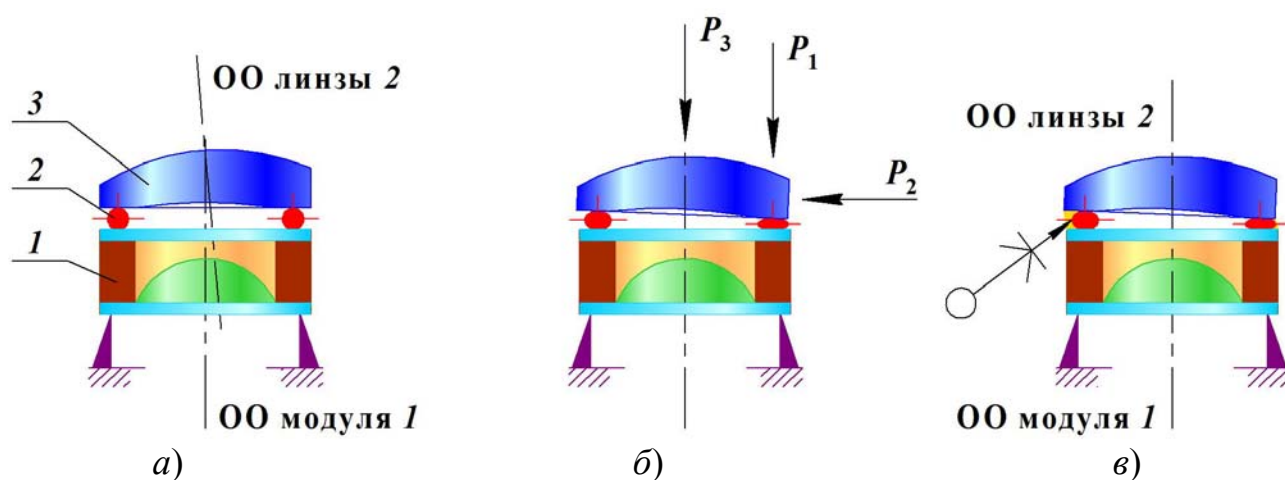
Принцип сборки и юстировки двухкомпонентного оптического блока с ЖЛМ
